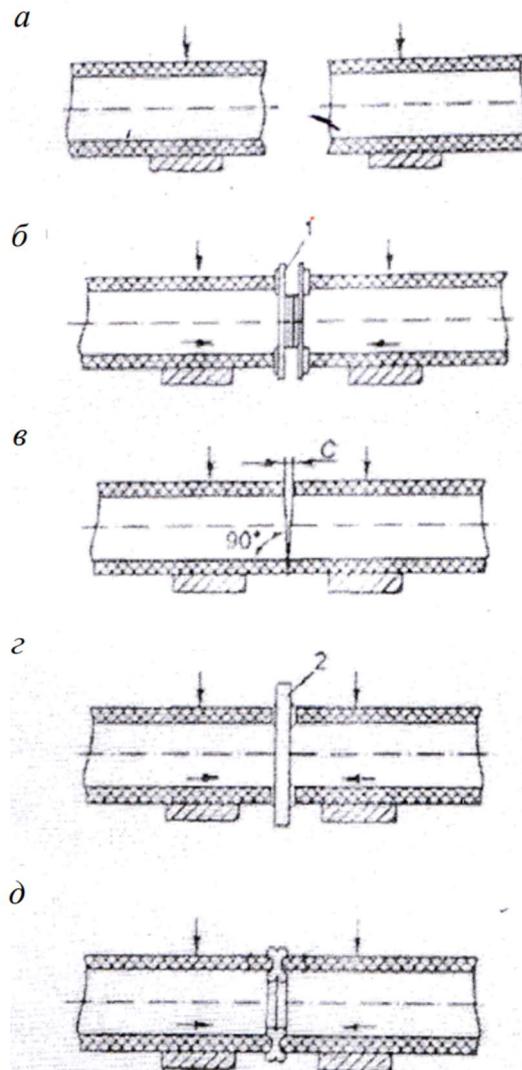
Последовательность процесса сборки и сварки встык труб из полиэтилена:
